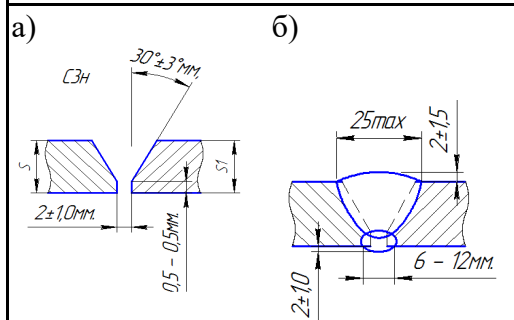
Размеры сварного соединения до (а) и после сварки (б)
